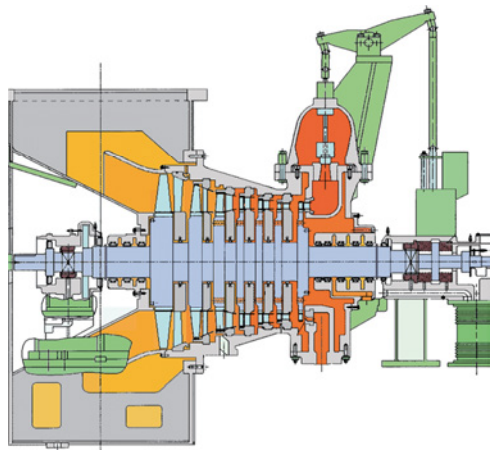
Turbína TGM Kanis Turbinen GmbH typu BT [16]
